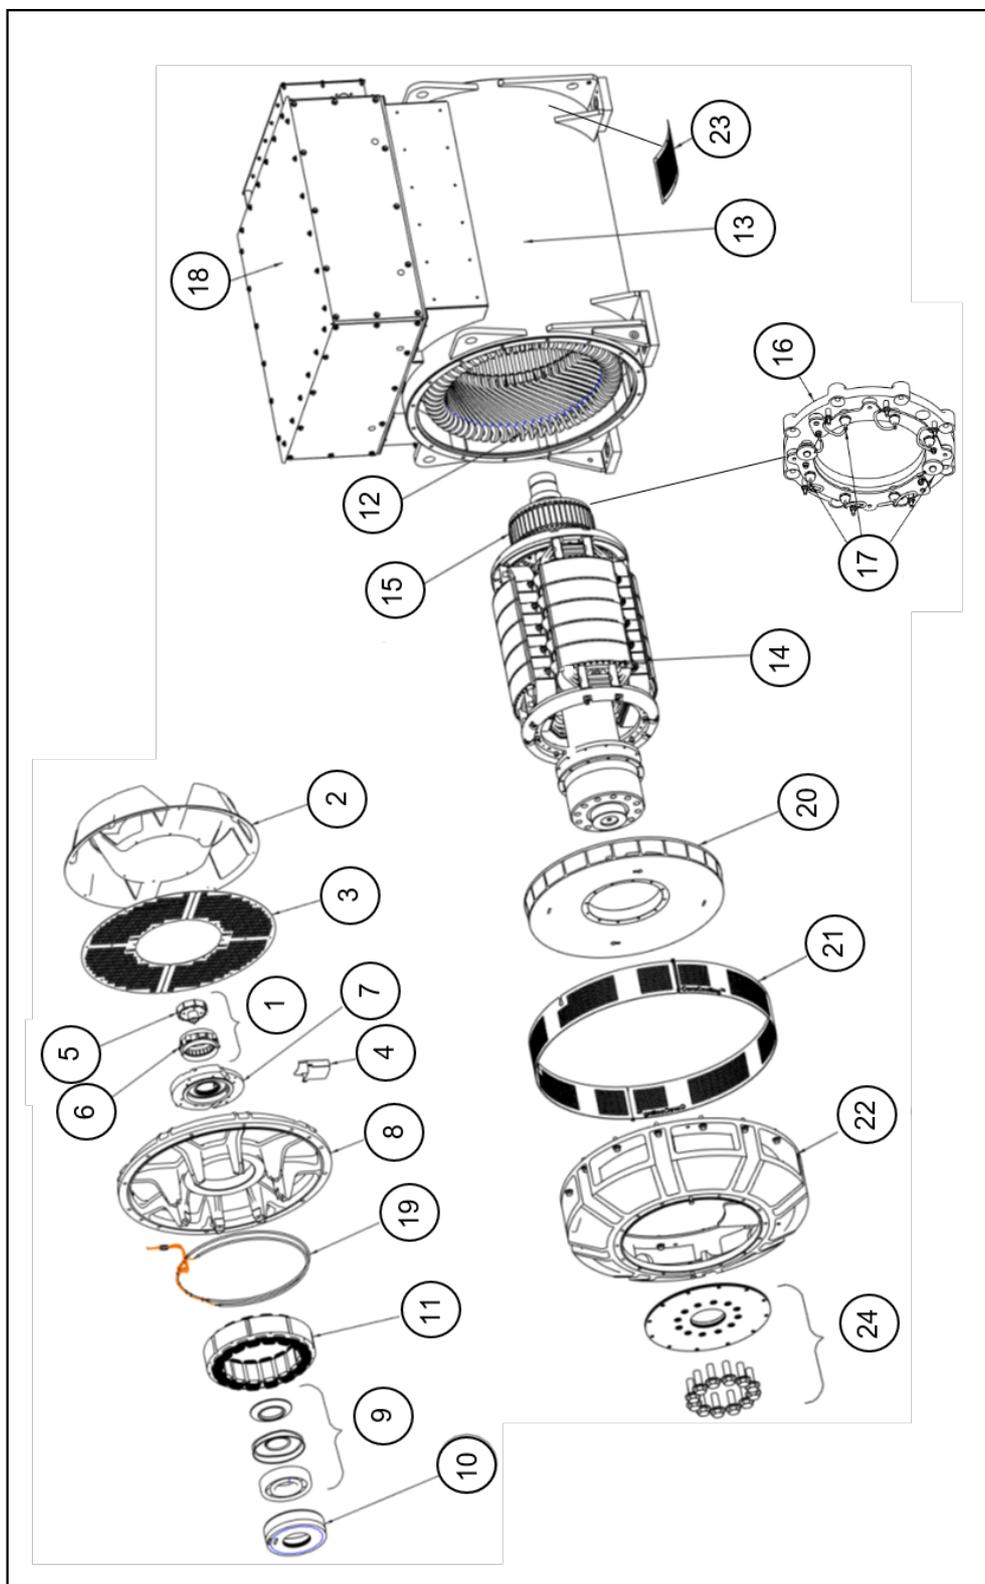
ALTERNADOR DE COJINETE ÚNICO S9
